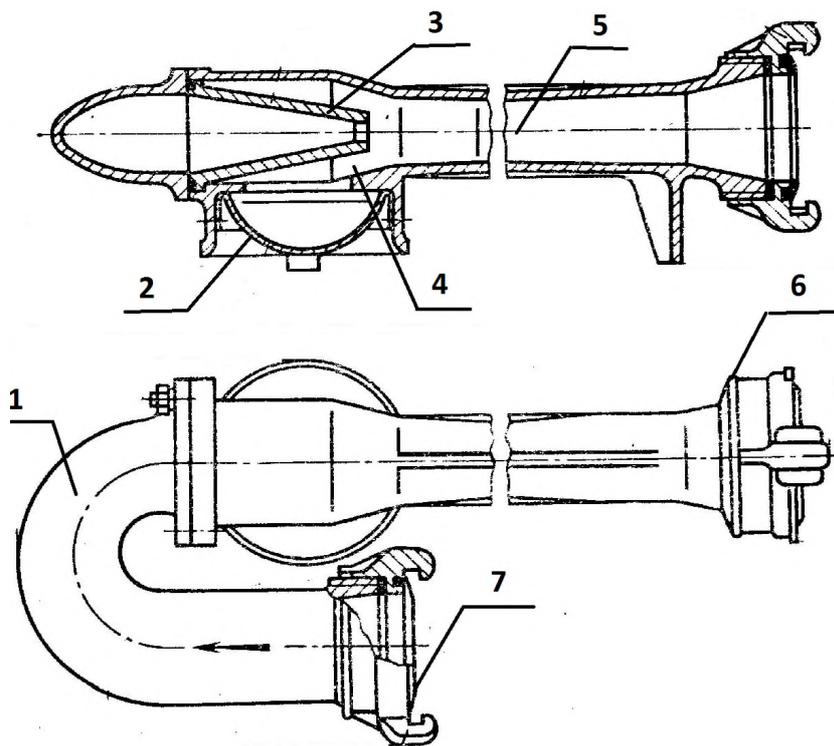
Гидроэлеватор пожарный Г- 600
